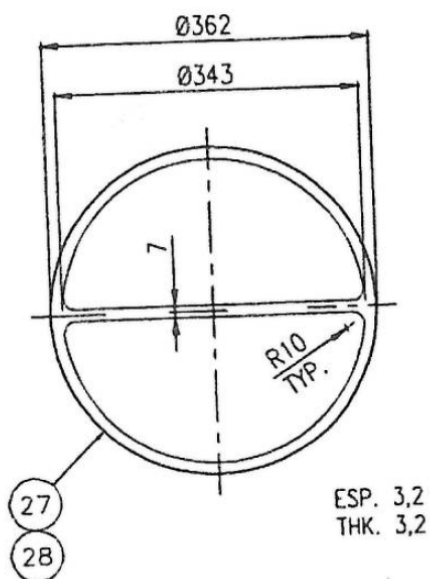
Plano de empaquetaduras enchaquetadas del 3E – 3204
